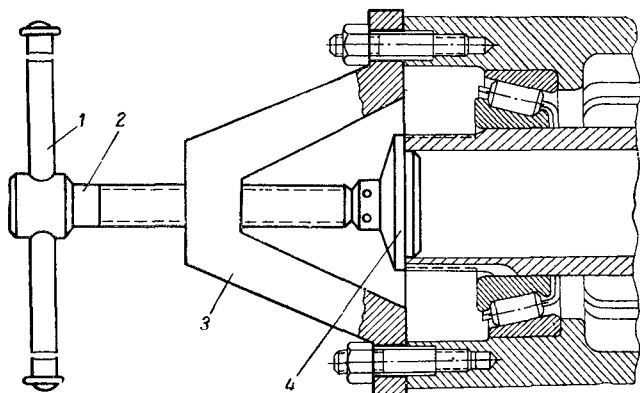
Приспособление для снятия ступицы заднего колеса:
